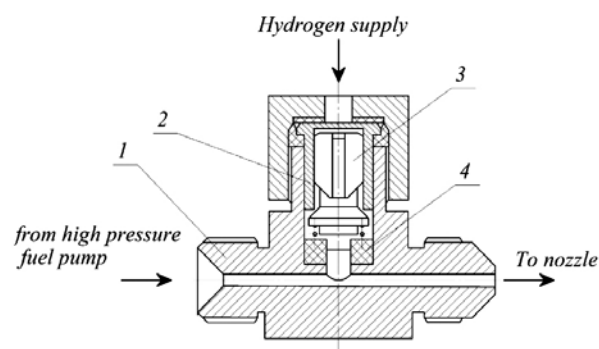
Пристрій подачі водню до магістралі високого тиску: 1 – корпус; 2 – втулка клапана; 3 – зворотний клапан із направляючими; 4 – посадочне кільце
